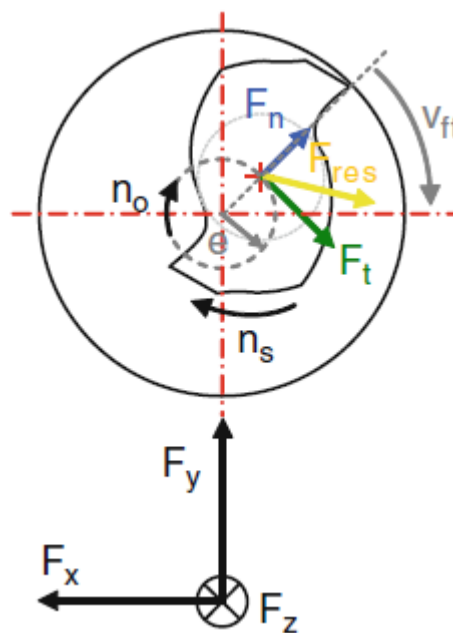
Geometrie frézovacích nástrojů [1]
